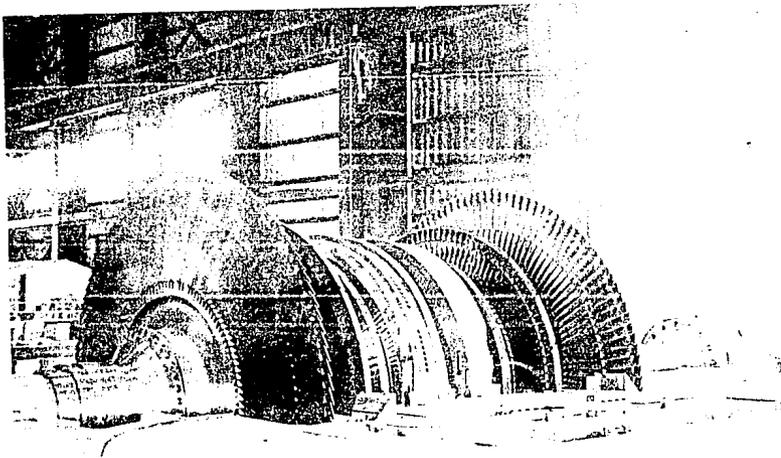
TURBINA DE BAJA PRESION SIN CARCAZA
